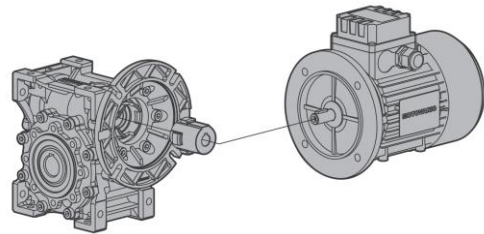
Esquema acoplamiento Motorreductor de tornillo sin fin.
